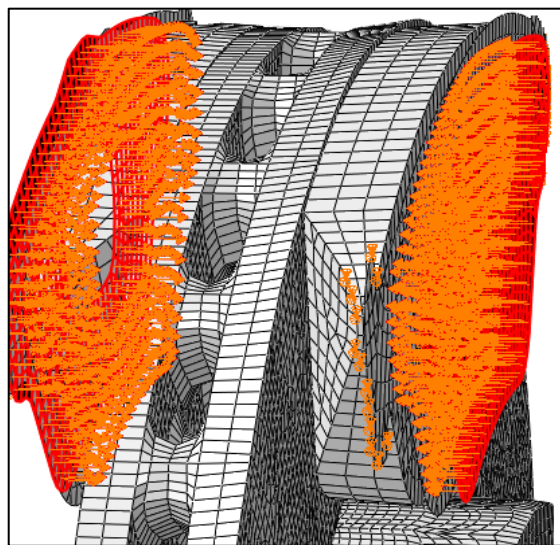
Aplicação da pressão simbolizada pelas setas laranjadas
